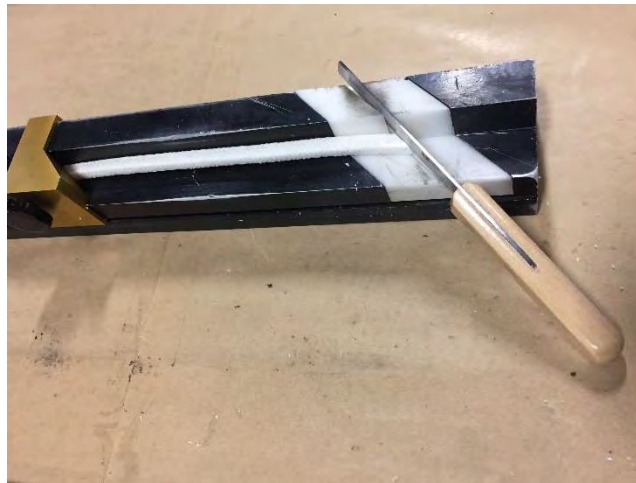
Mess- und Schneidwerkzeug für Stopfbuchspackungen
